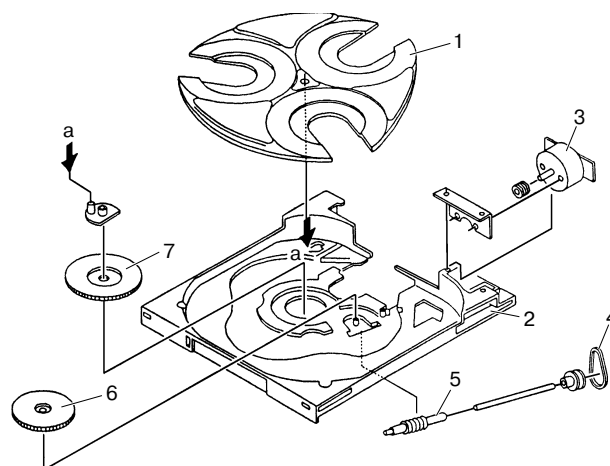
Механизм загрузки компакт-дисков с помощью поворотного стола
